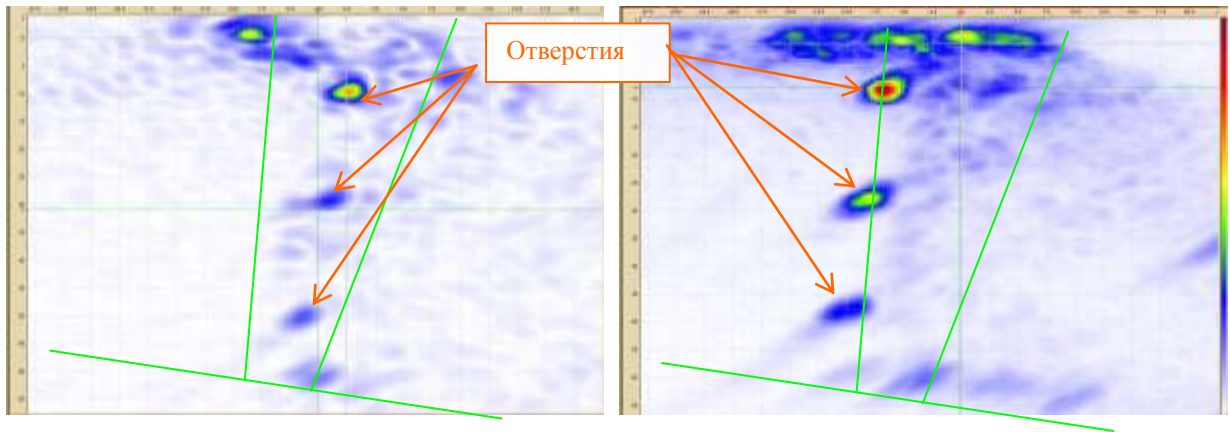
Схема контроля L60. Три отверстия бокового сверления Ø2 мм в центре сварного шва (левое изображение) и три отверстия бокового сверления Ø2 мм на кромке сварного шва (правое изображение). Наложена маска сварного шва.
